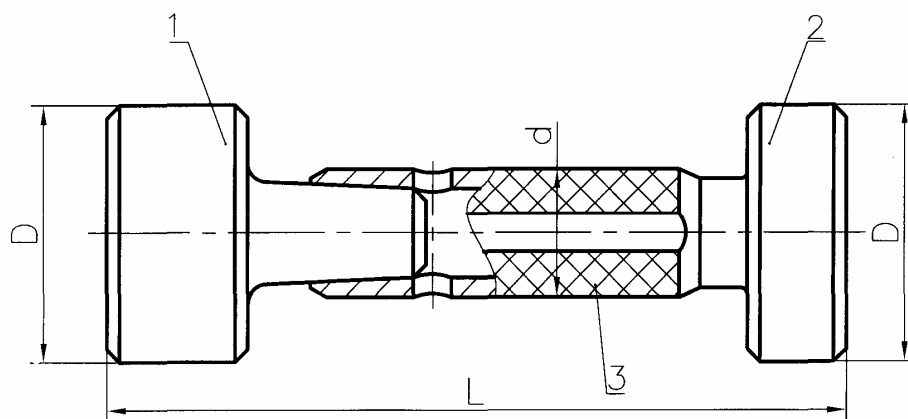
Калибр-пробка гладкий двусторонний со вставками:
